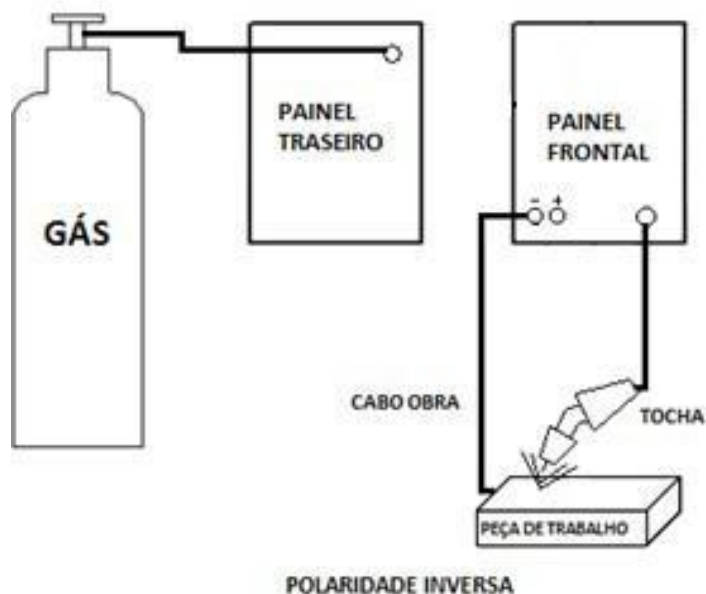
Diagrama conexão soldagem MIG/MAG.
